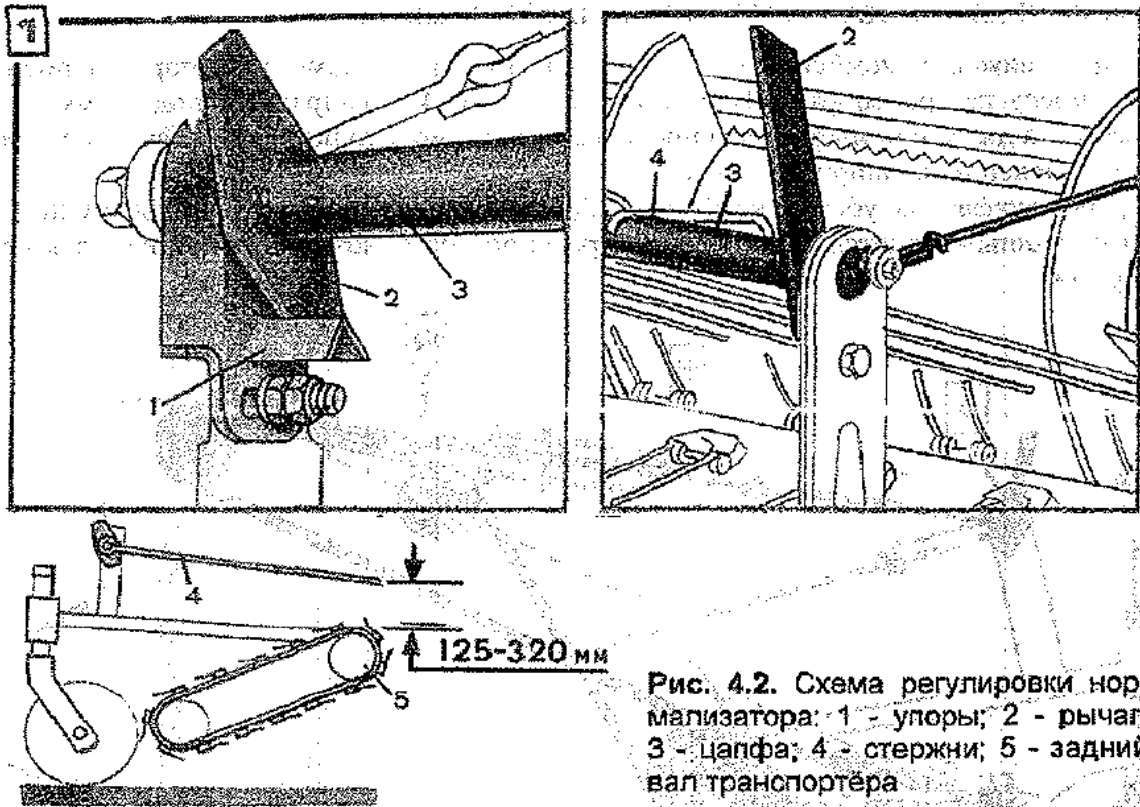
Схема регулировки нормализатора: 1 - упоры; 2 - рычаг; 3 - цапфа; 4 - стержни; 5 - задний вал транспортера
